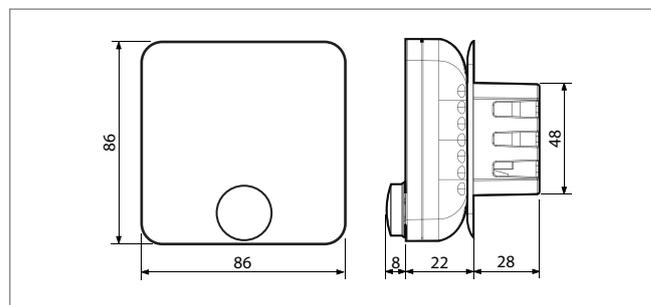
Dimensions pour l'élément de commande C-ZT pour un montage en saillie (dimensions en mm)
